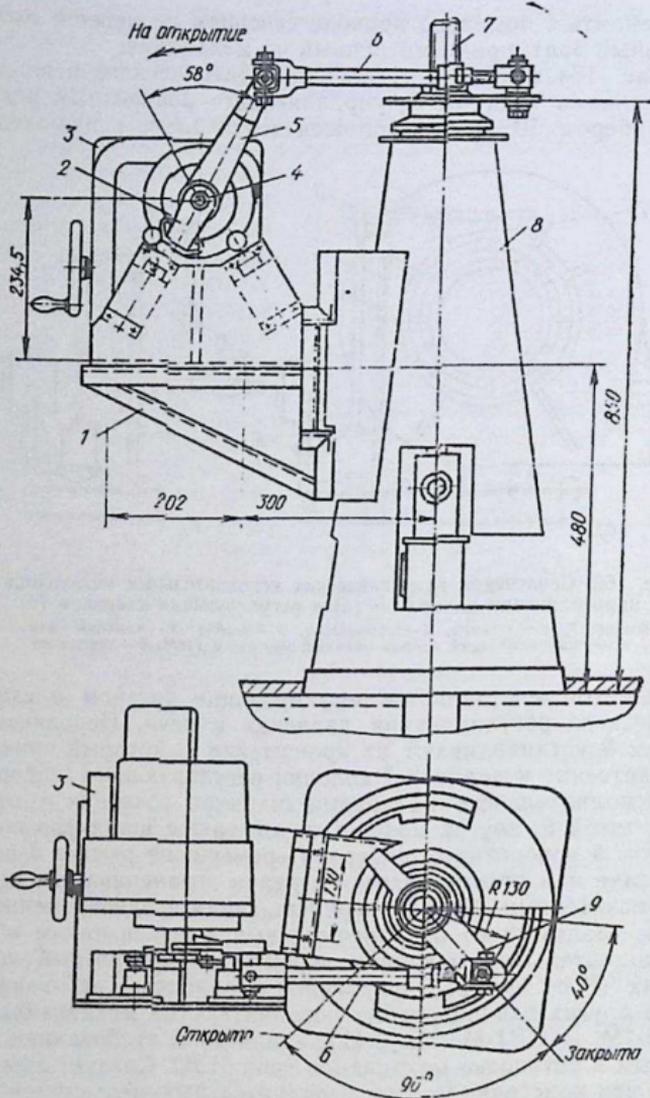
Установка электрического исполнительного механизма типа МЭО, управляющего поворотным регулирующим шибером: 1 — кронштейн, 2 — упор, 3 — исполнительный механизм, 4 — выходной вал исполнительного механизма, 5 — рычаг, 6 — соединительная тяга, 7 — выходной вал регулирующего шибера, 8 — корпус колонки регулирующего шибера, 9 — рычаг поворотного шибера
